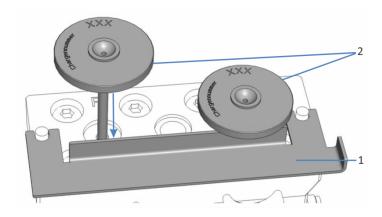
Installieren des Abstandswerkzeugs und der Kolben
